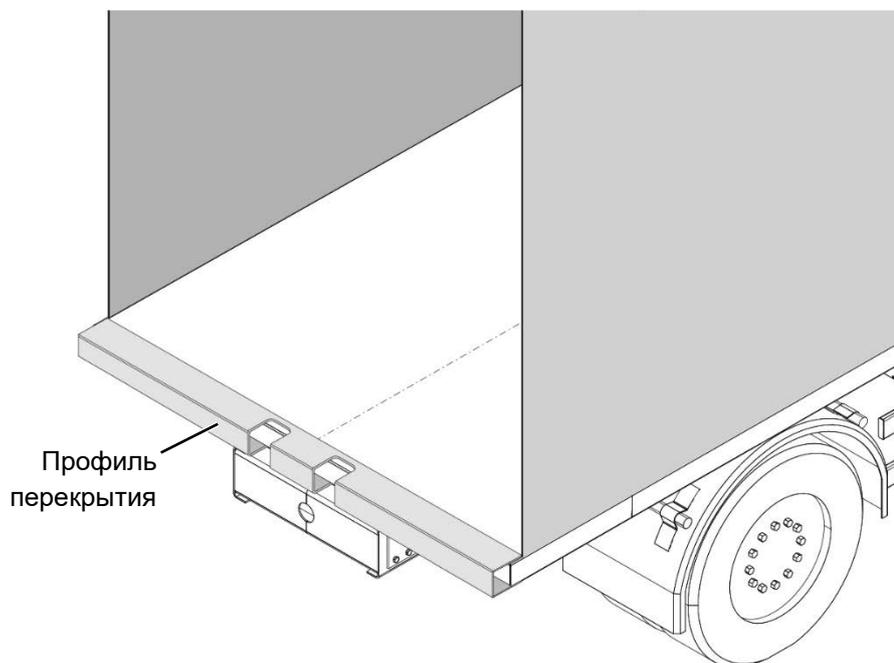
Профиль перекрытия с вырезами для дверных шарниров
